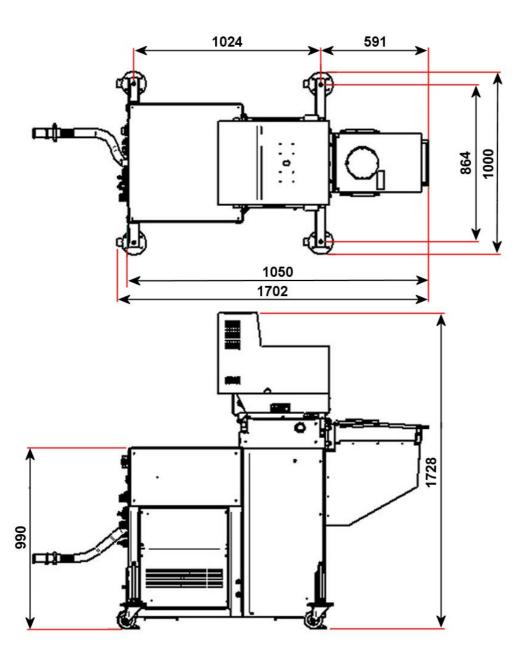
Габаритные размеры системы с установленными транспортными колесами
